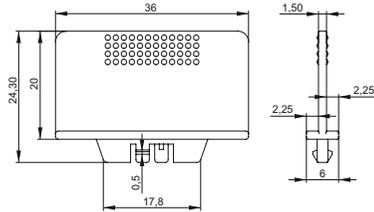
Габаритные размеры перегородки / Figure 3 – Overall dimensions of the separating plate
